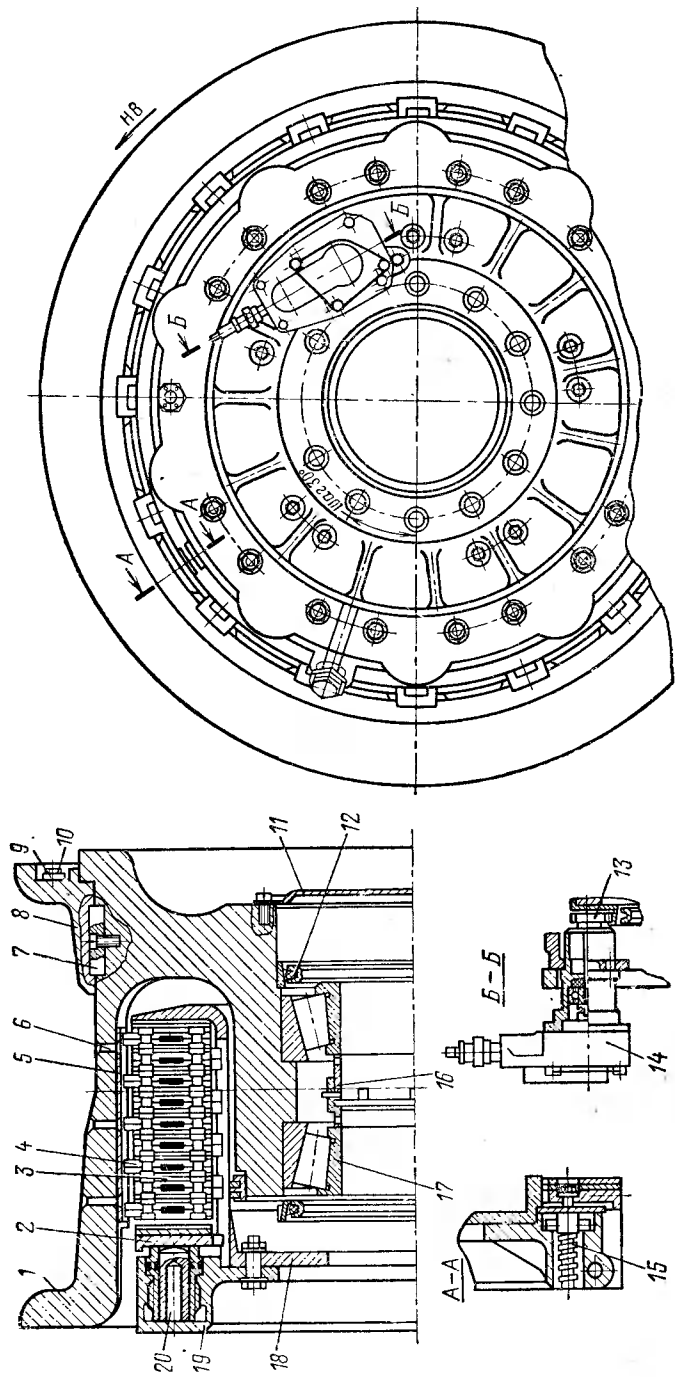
Конструкция колеса с дисковым тормозом:
